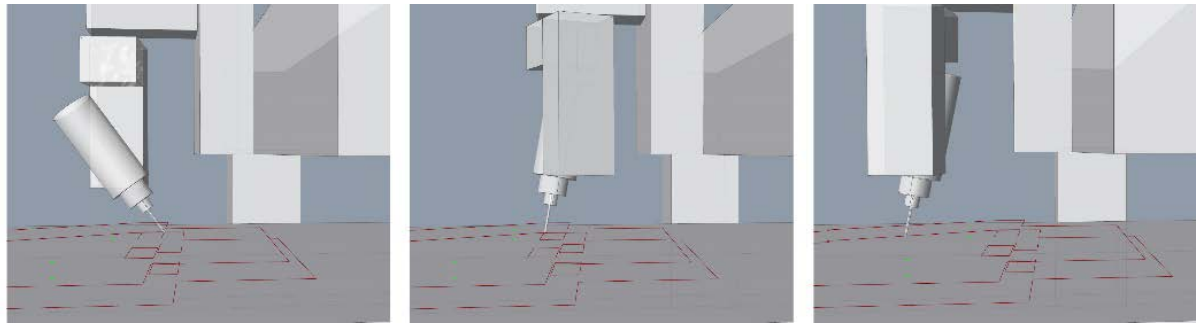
Simulation der Maschinenbewegungen im CAD Plugin: Die Herstellung der Plattenbauteile mit konkaven Eckpunkten und unterschiedlich schrägen Flanken erfolgt mittels 5-Achs Simultanbearbeitung. Das Werkzeug wird um beide Rotationsachsen des CNC Bearbeitungszentrums gedreht, während gleichzeitig eine Translationsbewegung erfolgt.
